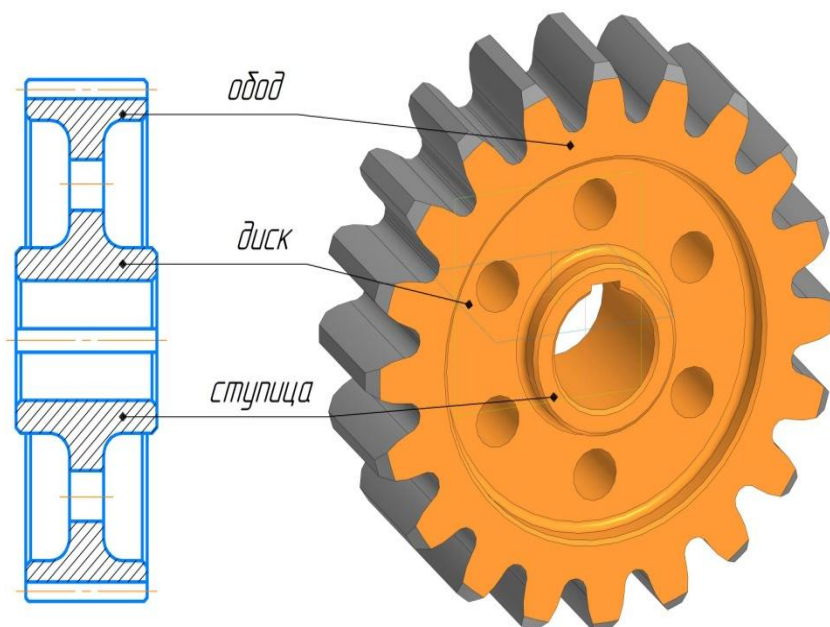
Основные конструктивные элементы зубчатого колеса
